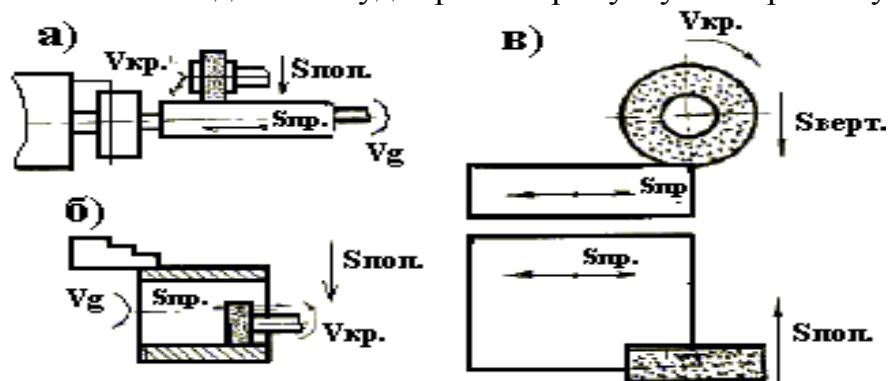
Схемы шлифования: а) наружное круглое; б) внутреннее круглое; в) плоское.
